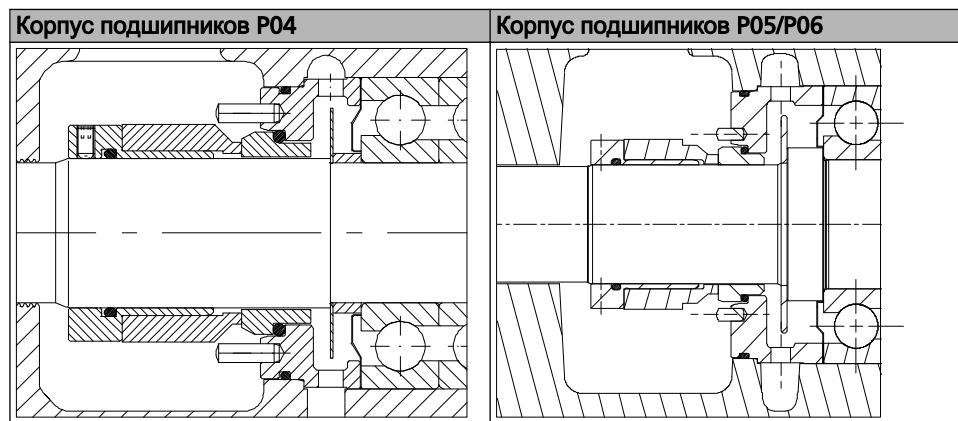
Обзорный чертёж НПК-LS/LE/LS4/LE4
